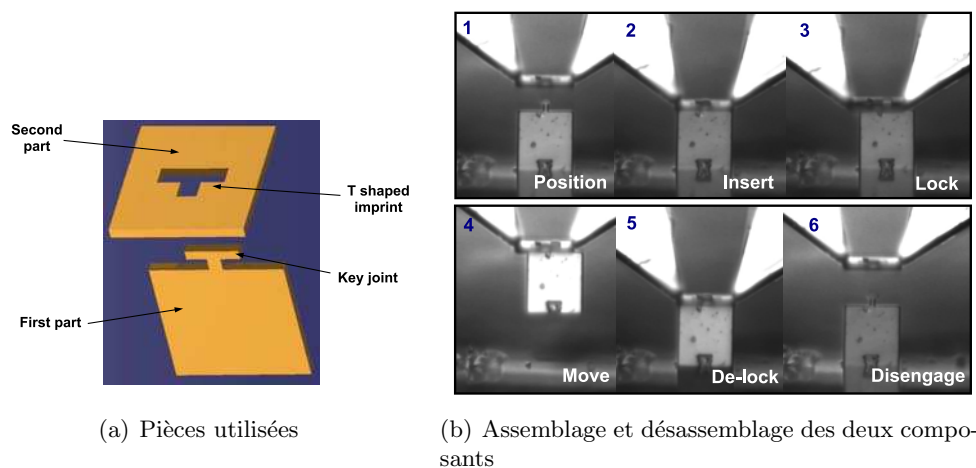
Exemple d'assemblage d'objets tests possédant un verrou mécanique
